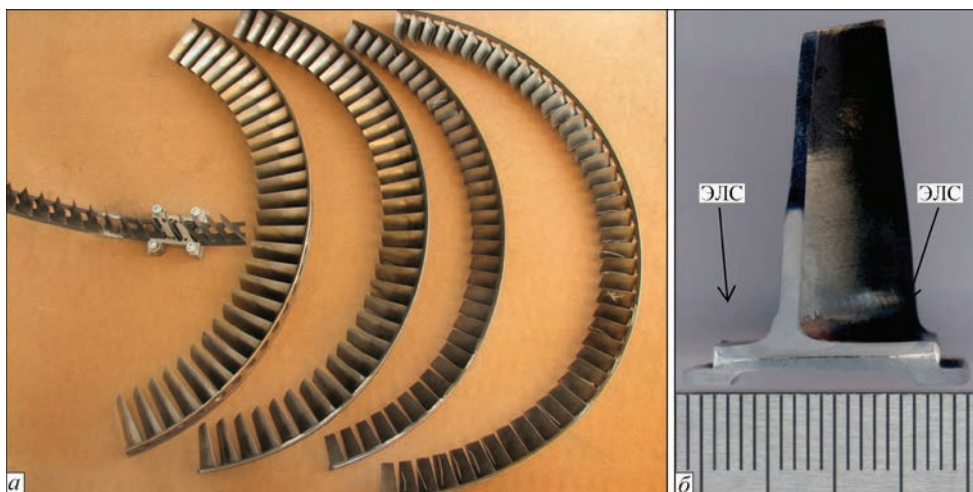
Схема сборки лопатки-донора с полукольцом (а) и макрошлиф сварного соединения (б) направляющего аппарата статора компрессора высокого давления
